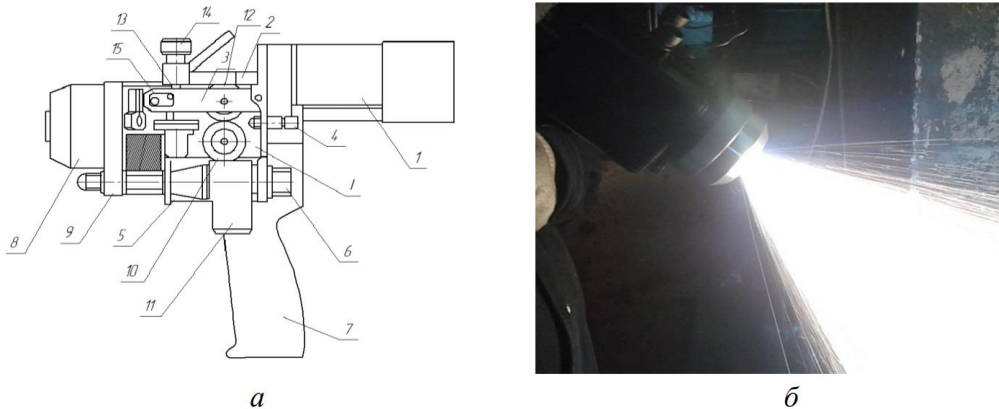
Загальний вигляд металізатора: а - пристрій металізатора; б - установка в роботі.
